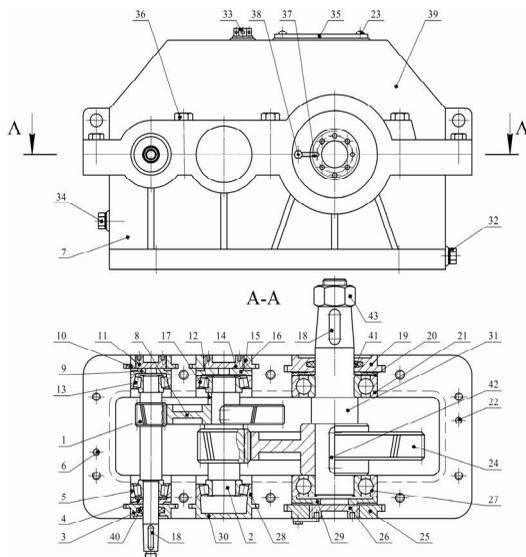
Конструкция двухступенчатого цилиндрического редуктора:
